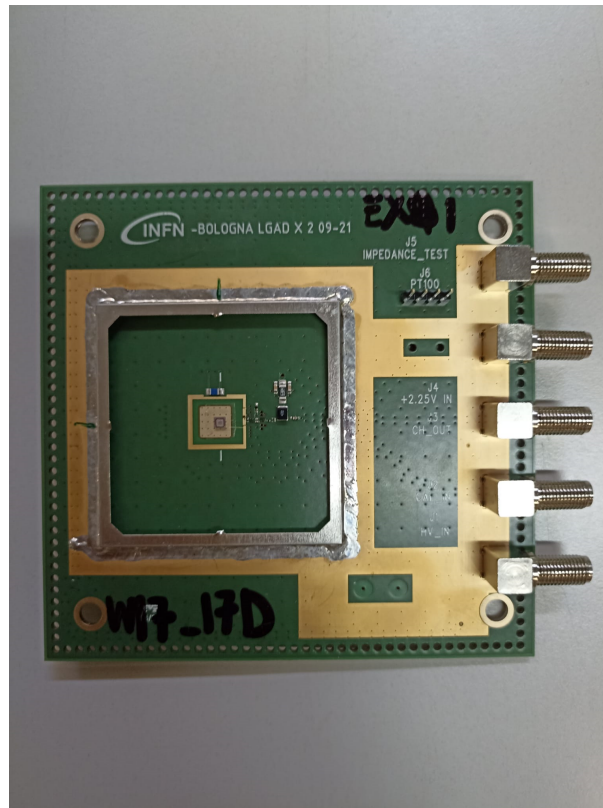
In questa foto è possibile vedere il lato frontale della scheda elettronica, dove è stato montato uno dei due sensori LGAD della coppia.
